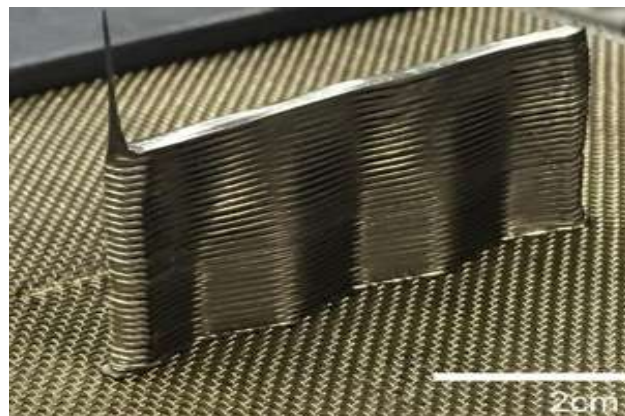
Obiect din metal obținut prin printarea 3D [3]
